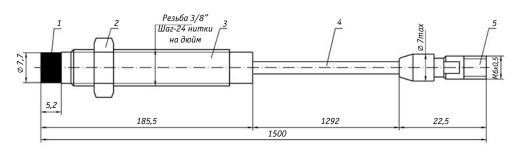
Преобразователь вихретоковый ИЦФР.408113.018 (код ПВ29): 1 – наконечник; 2 – гайка; 3 – корпус; 4 – кабель; 5 – розетка СР-50-106ФВ
